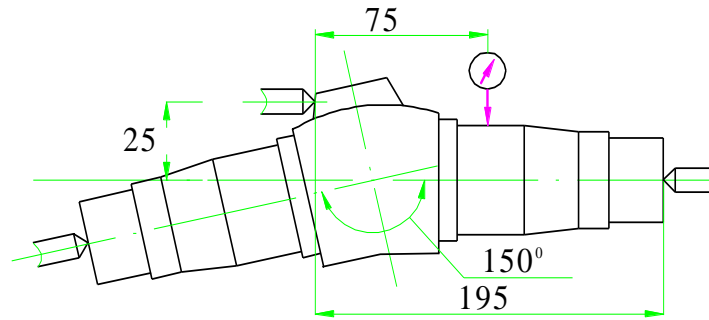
Схема замірювання точності обробки циліндричних поверхонь кривих вісей.
